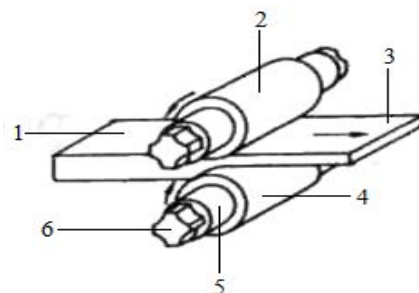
Схема продольной прокатки металла: 1– прокатываемая заготовка, 2 – верхний валок, 3 – направление прокатки, 4 – нижний валок, 5 – шейка валка, 6 – трещина валка.
